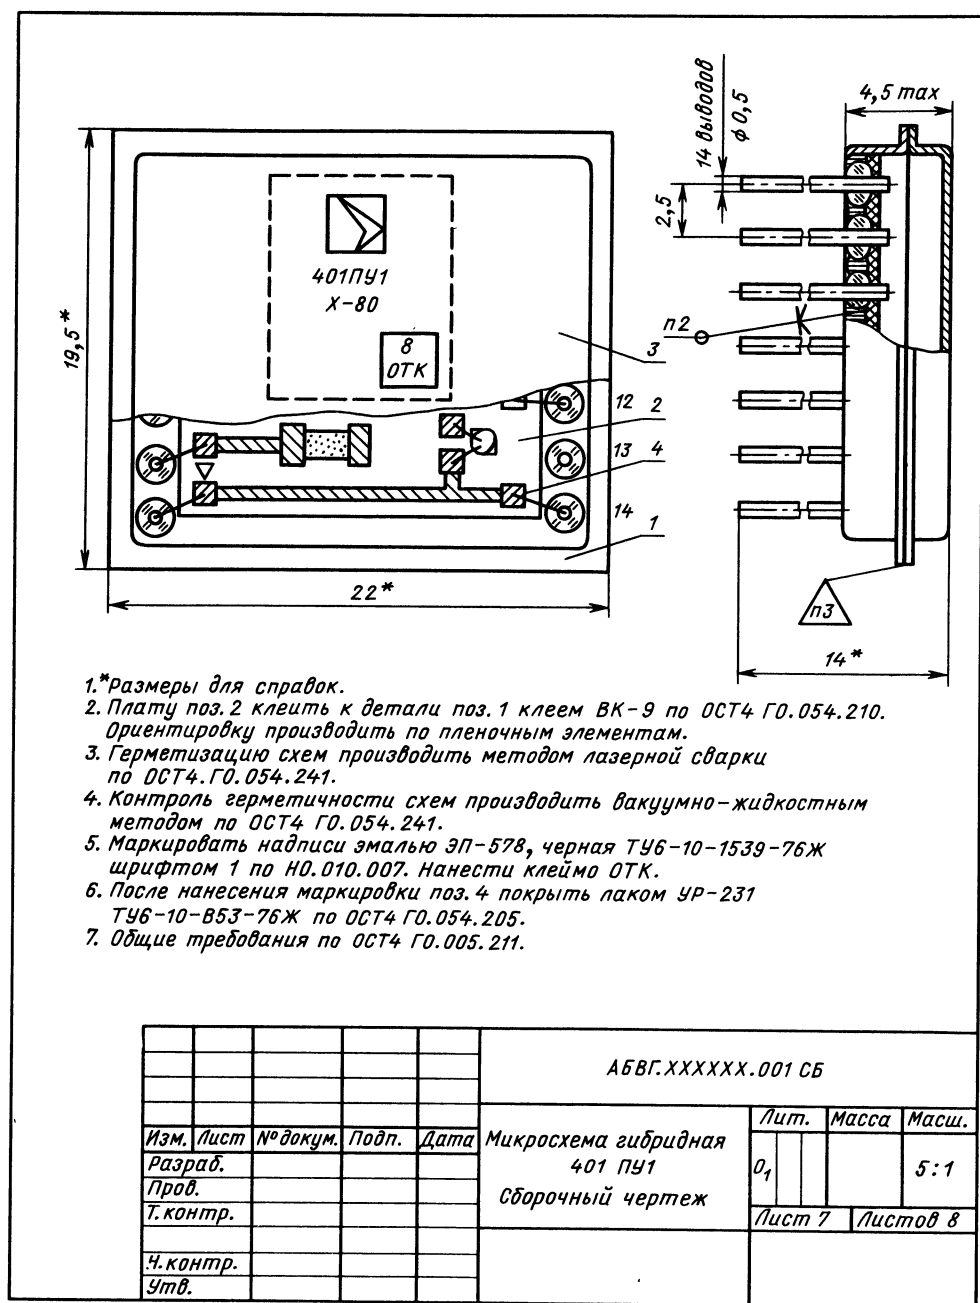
Сборочный чертеж тонкопленочной микросхемы
